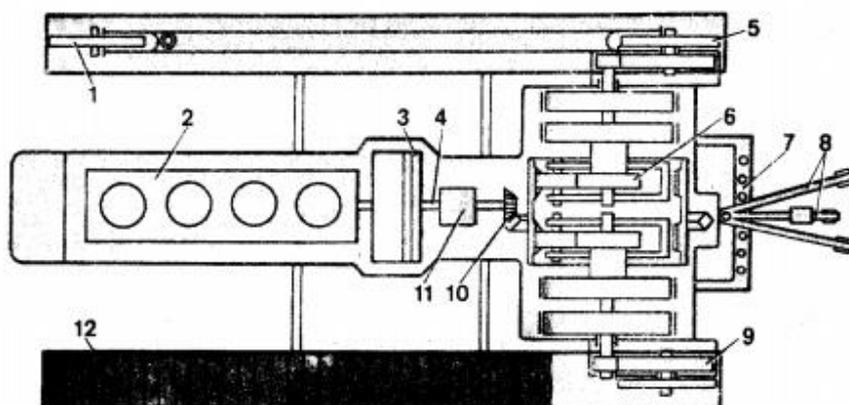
Расположение основных частей, их механизмов и деталей гусеничного трактора ДТ-75МВ:
